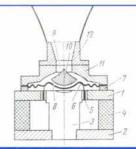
Основные элементы конструкции узкогорлого рупора: 1 — верхний фланец; 2 — нижний фланец; 3 керн; 4 - магнит; 5 - звуковая катушка; 6 — диафрагма; 7 — крепящие кольца; 8 — предрупорная камера; 9 — горло рупора; 10 — вкладыш; 11 — крышка; 12 — рупор
